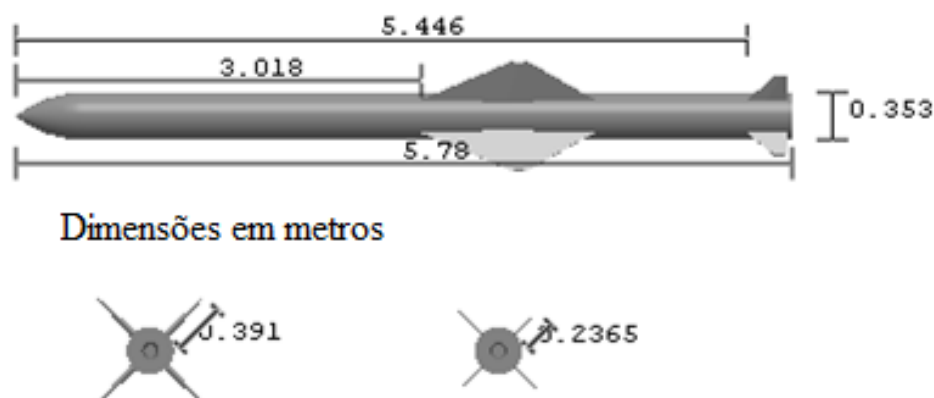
Desenho do míssil com dimensões físicas principais.
